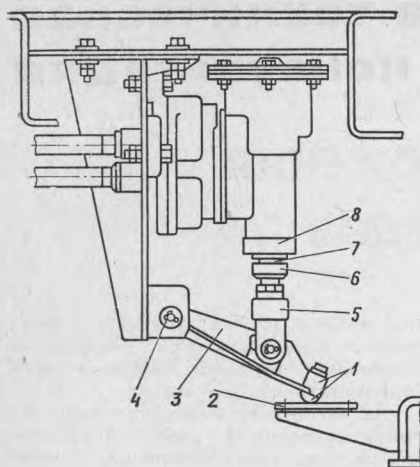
Соединение вилки авторежима с опорным рычагом привода на вагонах дизель-поездов серии ДР-1: 1 — вилка авторежима; 2 — контргайка; 3 — муфта; 4 — цапфа; 5 — валик; 6 — опорный рычаг
